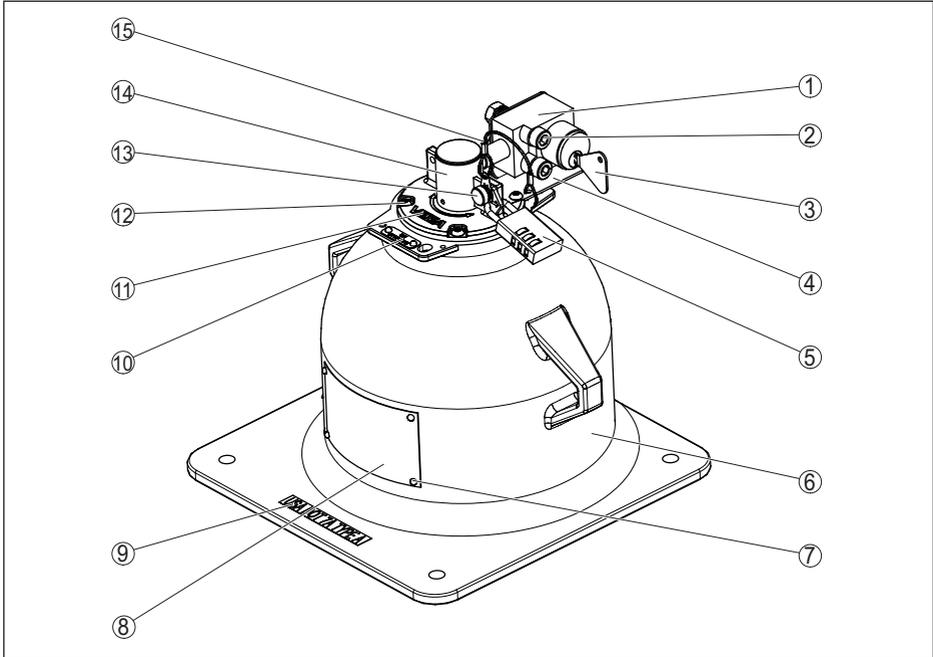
Werkstoffe VEGASOURCE 83 - Ausführung X, C - mit Interlock-Schalter
